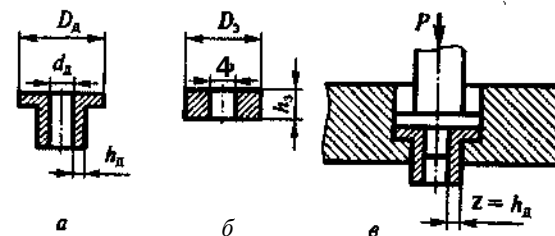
Прямое холодное выдавливание: а - деталь; б - заготовка; в - схема процесса
